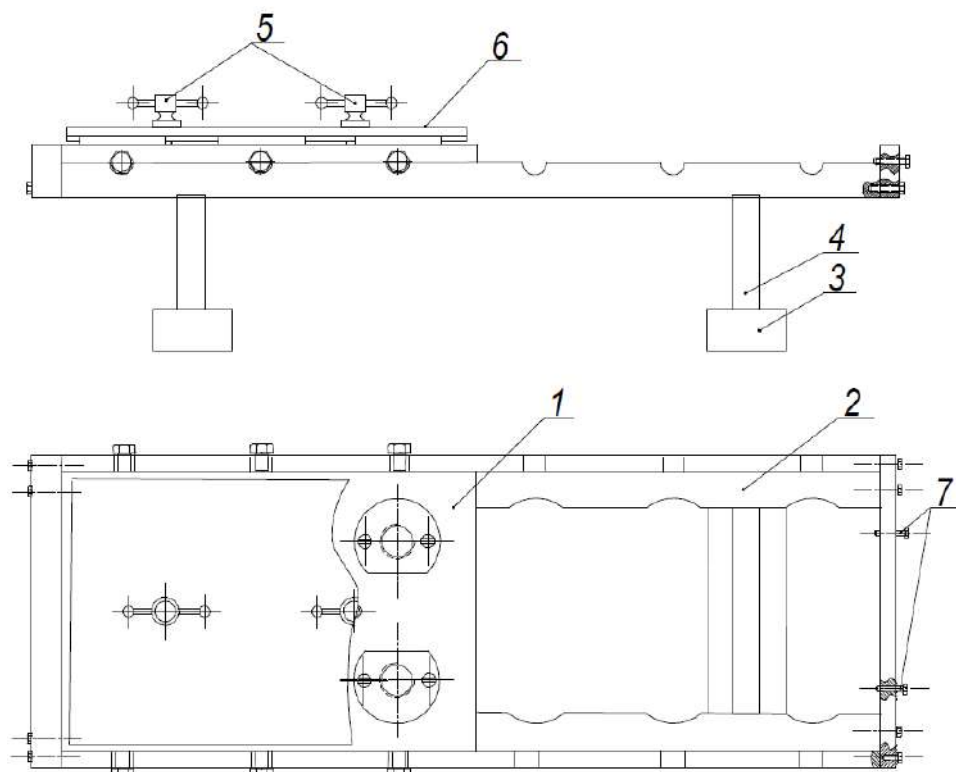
Приспособление для шлифования и притирки уплотнительных торцов корпусов форсунок:
